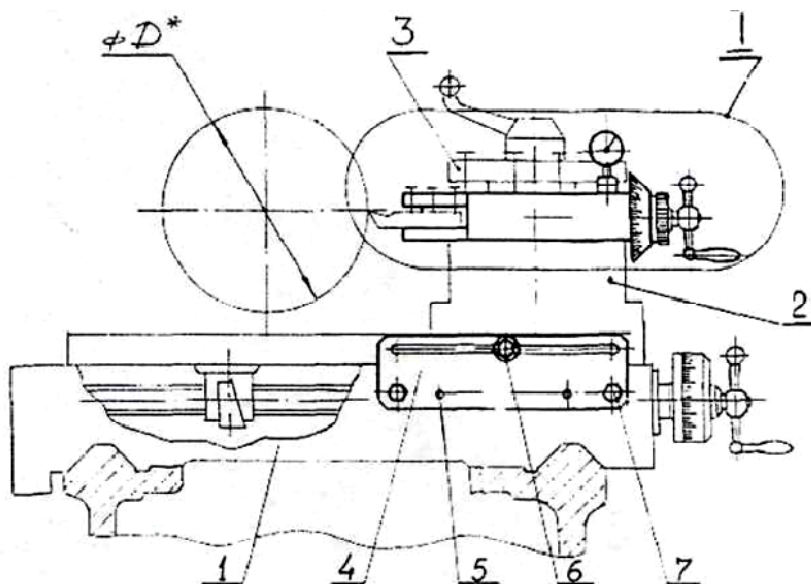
Розташування вузлів пристрою поперечної подачі для токарних верстатів.
